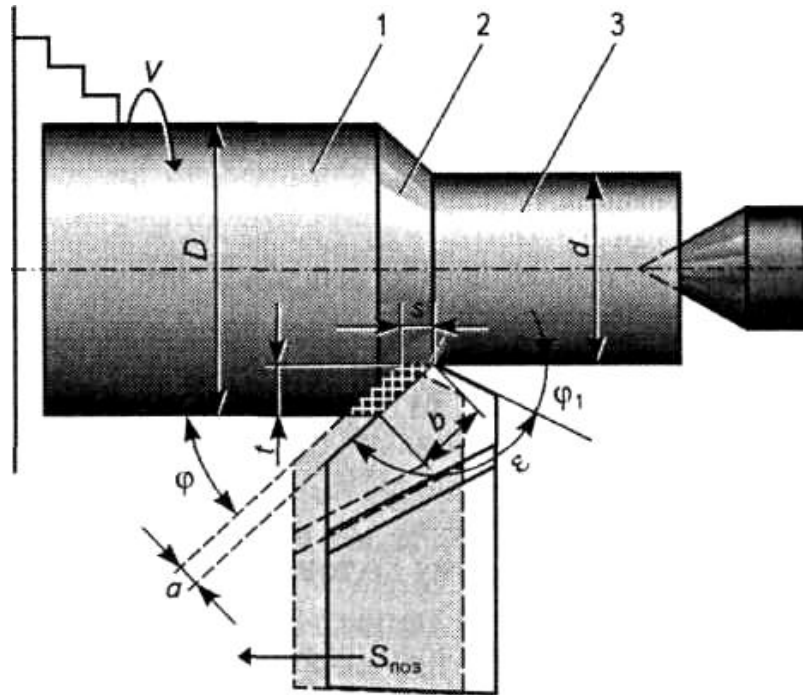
Елементи різання і геометрія шару металу, що зрізується:
